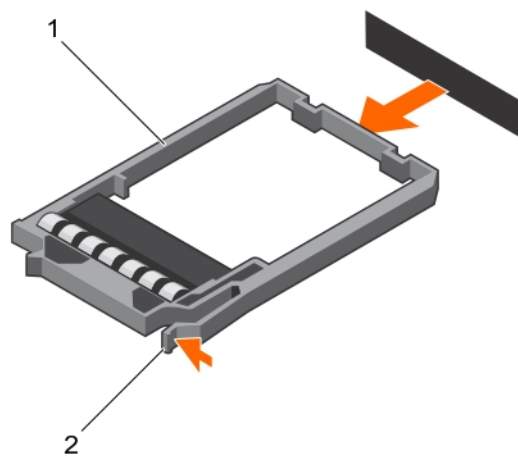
Entfernen einer 1,8-Zoll-SSD-Laufwerkplatzhalterkarte
